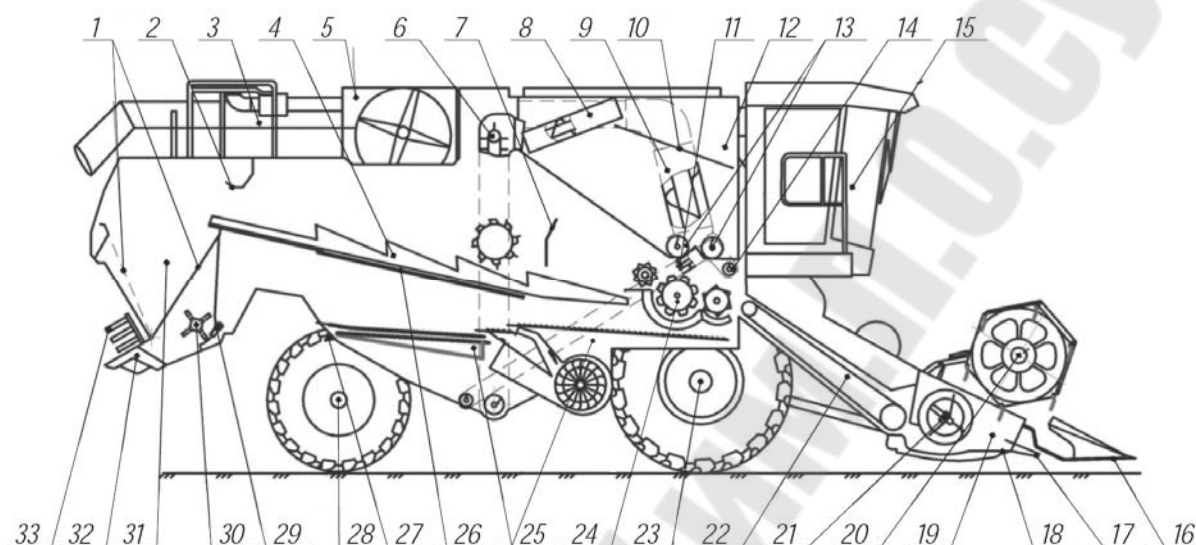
Конструктивная схема зерноуборочного комбайна КЗ-14 с жаткой:
